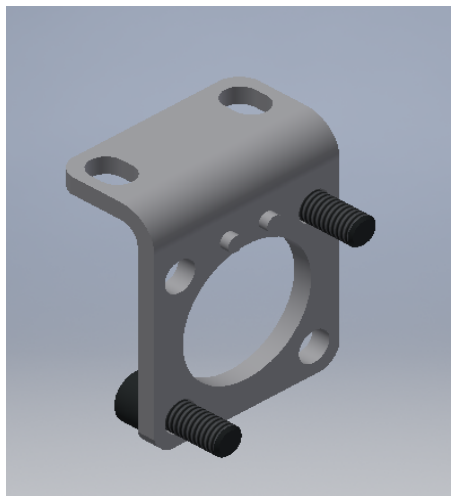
Montaje utilizado para el actuador neumático de la fase 2.
